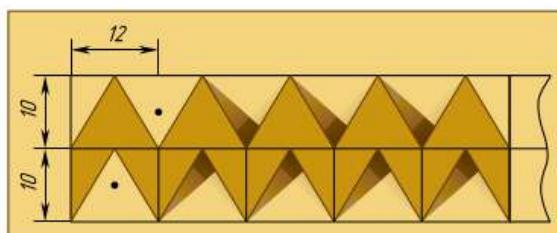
Образец учебной заготовки, выполненный в технике резьбы сколышков поперёк, вдоль и под углом к волокнам
